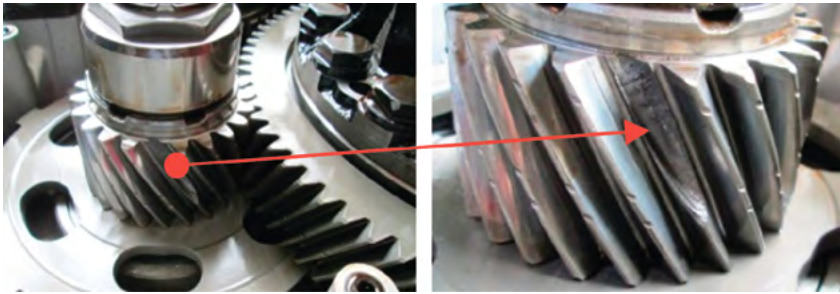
Вылом фрагмента зуба ведущей шестерни главной передачи автомобиля
